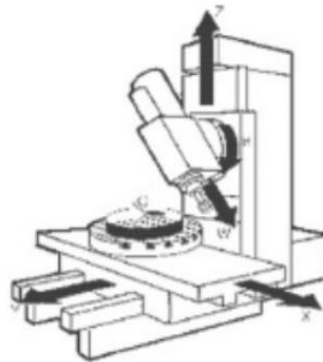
Centro de mecanizado horizontal con seis ejes [9].
